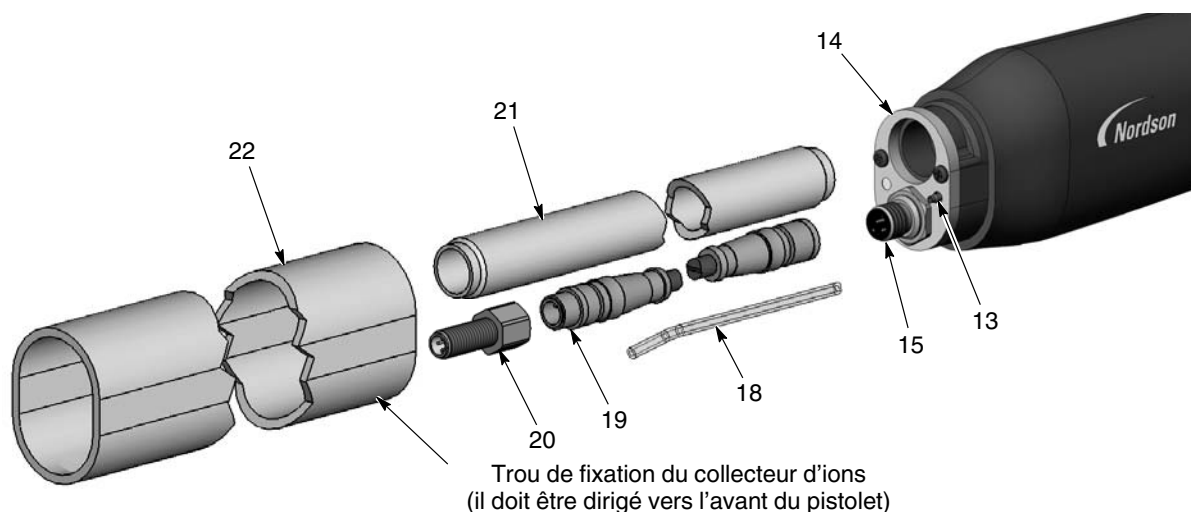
Démontage du pistolet à fixation sur tube 2 sur 5
